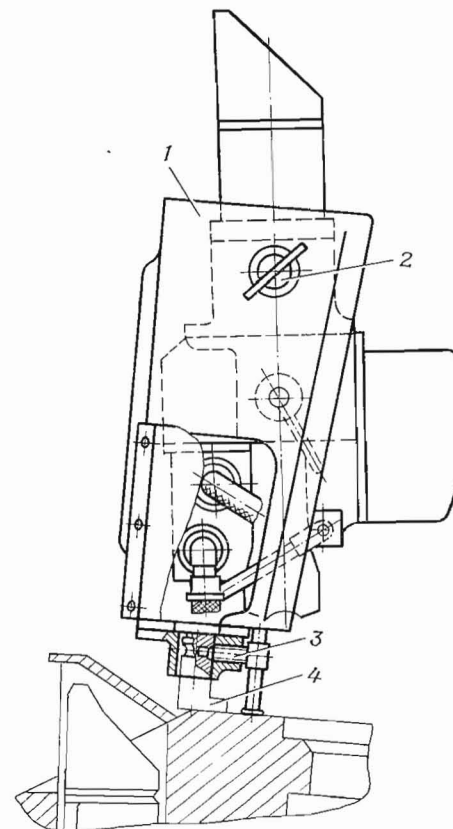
Установка прибора ТВНЕ-4Б по-походному:
